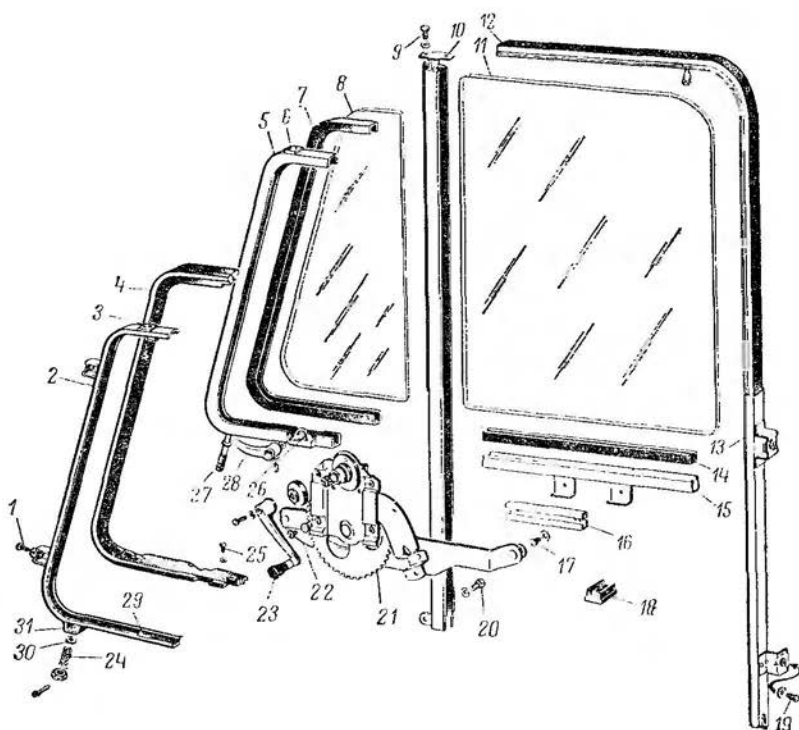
Опускающее стекло и поворотная вентиляция двери:
